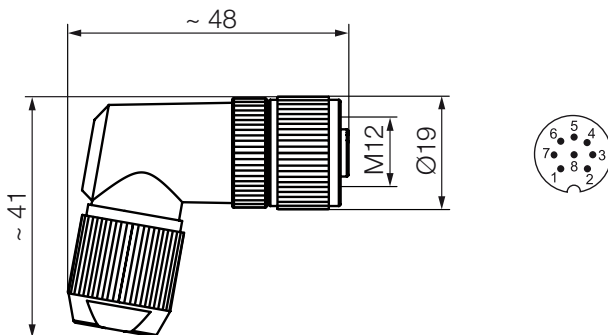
Steckverbinder BCC M488-0000-10-000-43x834-000
